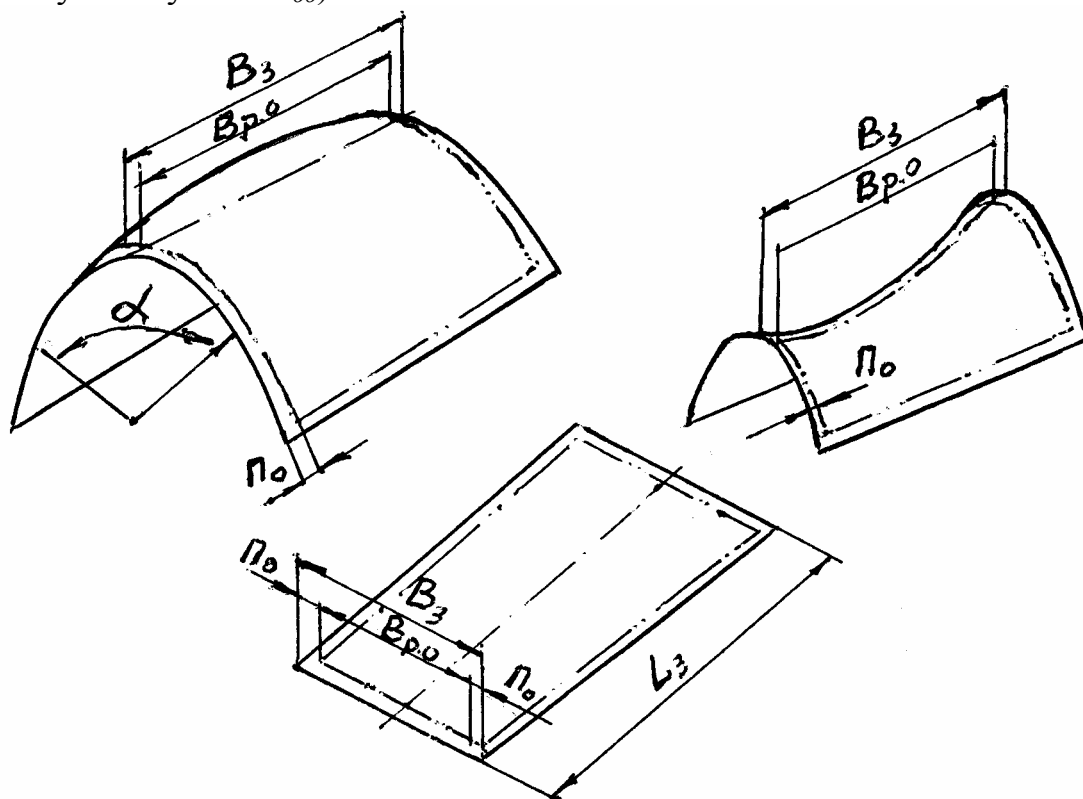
Схема определения ширины заготовки обшивки двойной кривизны при обтяжке
